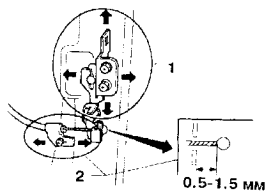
Регулировка тросика и фиксатора замка крышки багажника для моделей с кузовом "Седан" (См. Раздел 18)
